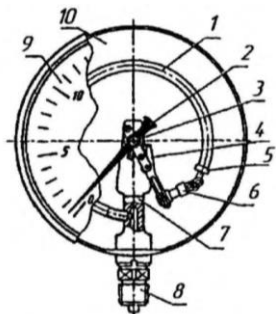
Манометр с одновитковой трубчатой пружиной
